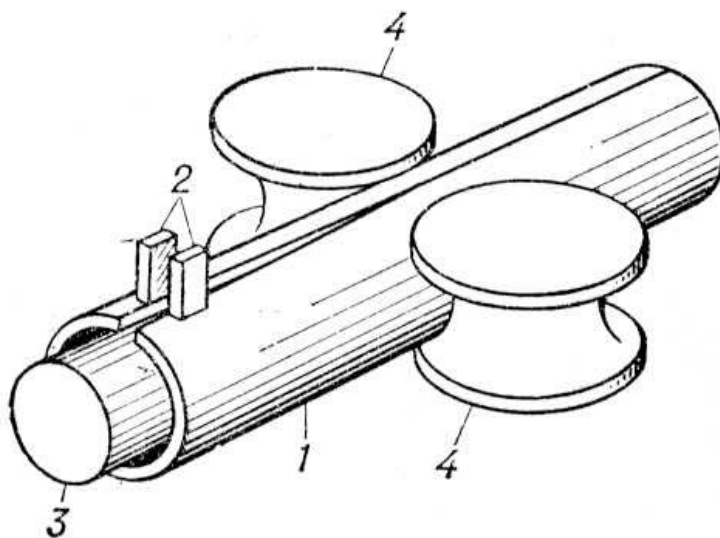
Схема сварки труб контактным способом
